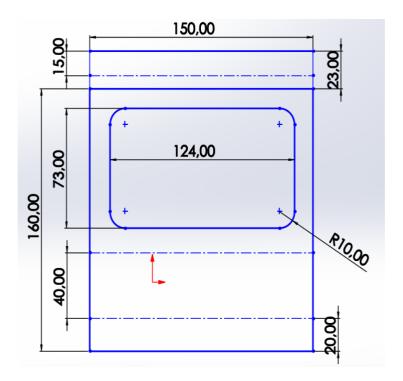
Vista Superior del Diseño de la Cabina del Tractor CAMECO 505
